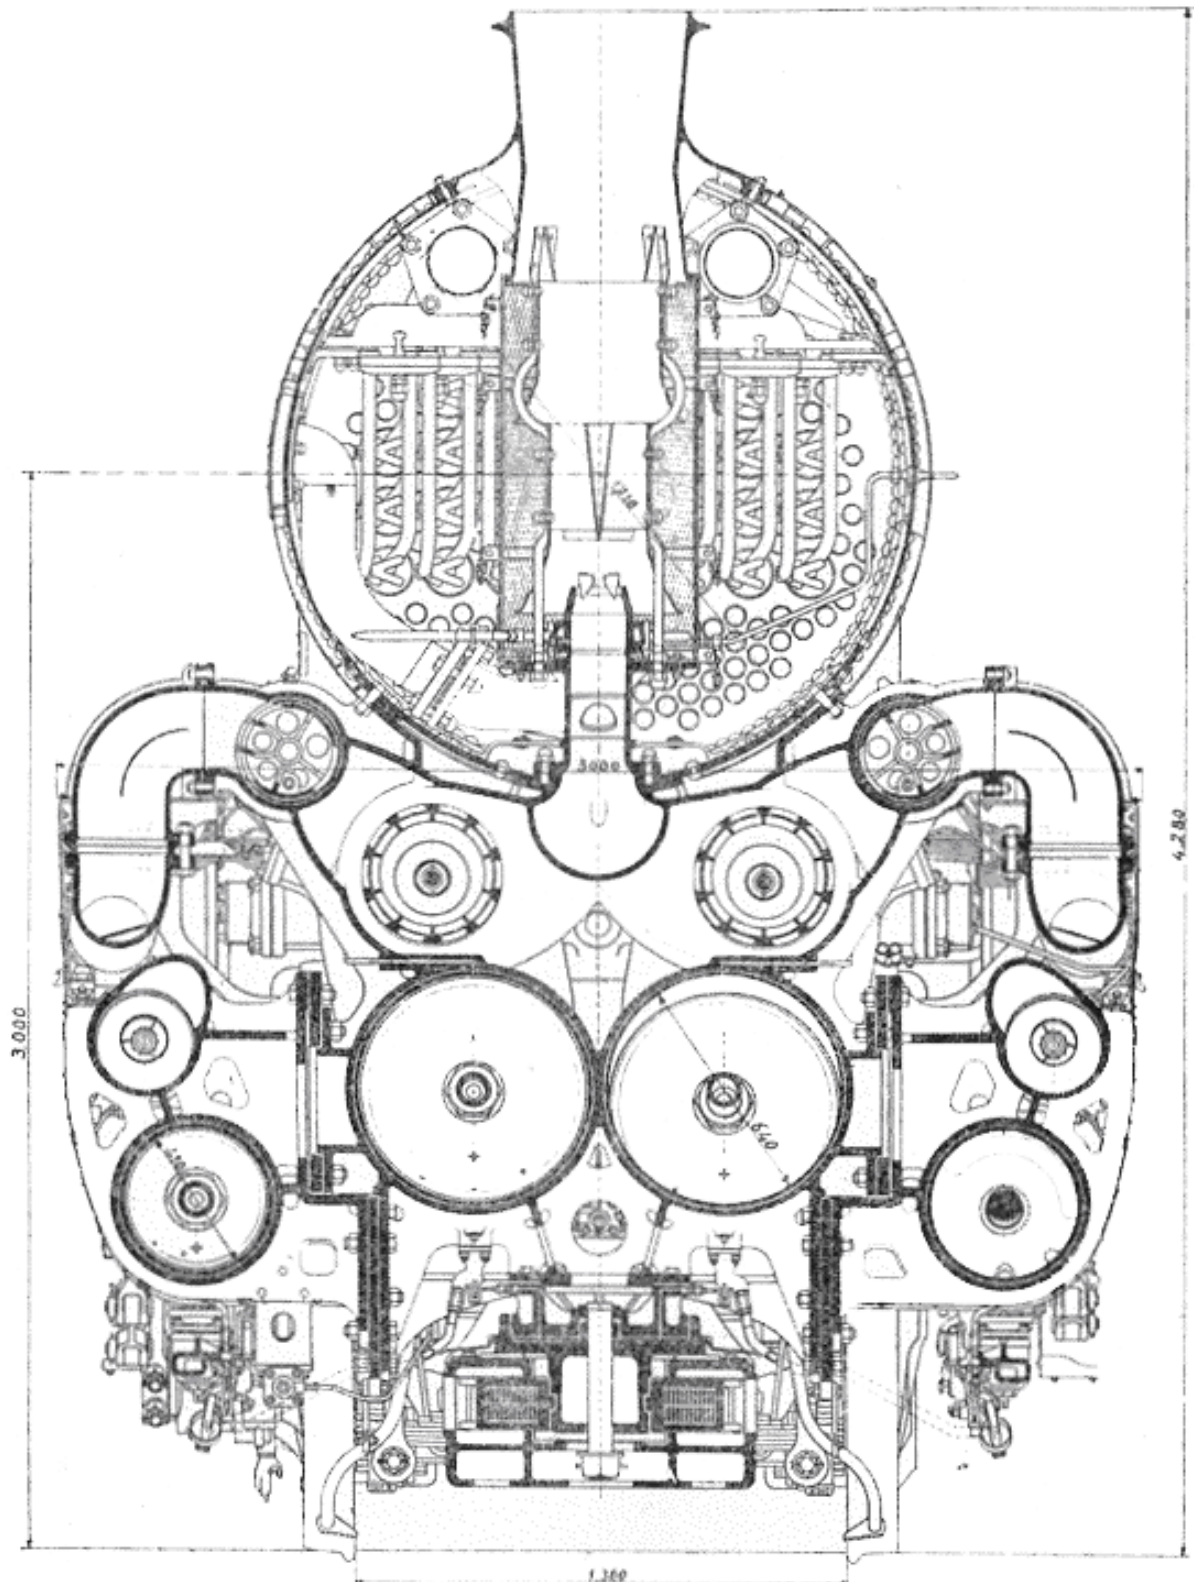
Corte por el macizo de los cilindros de las locomotoras 141 P de la S.N.C.F.
